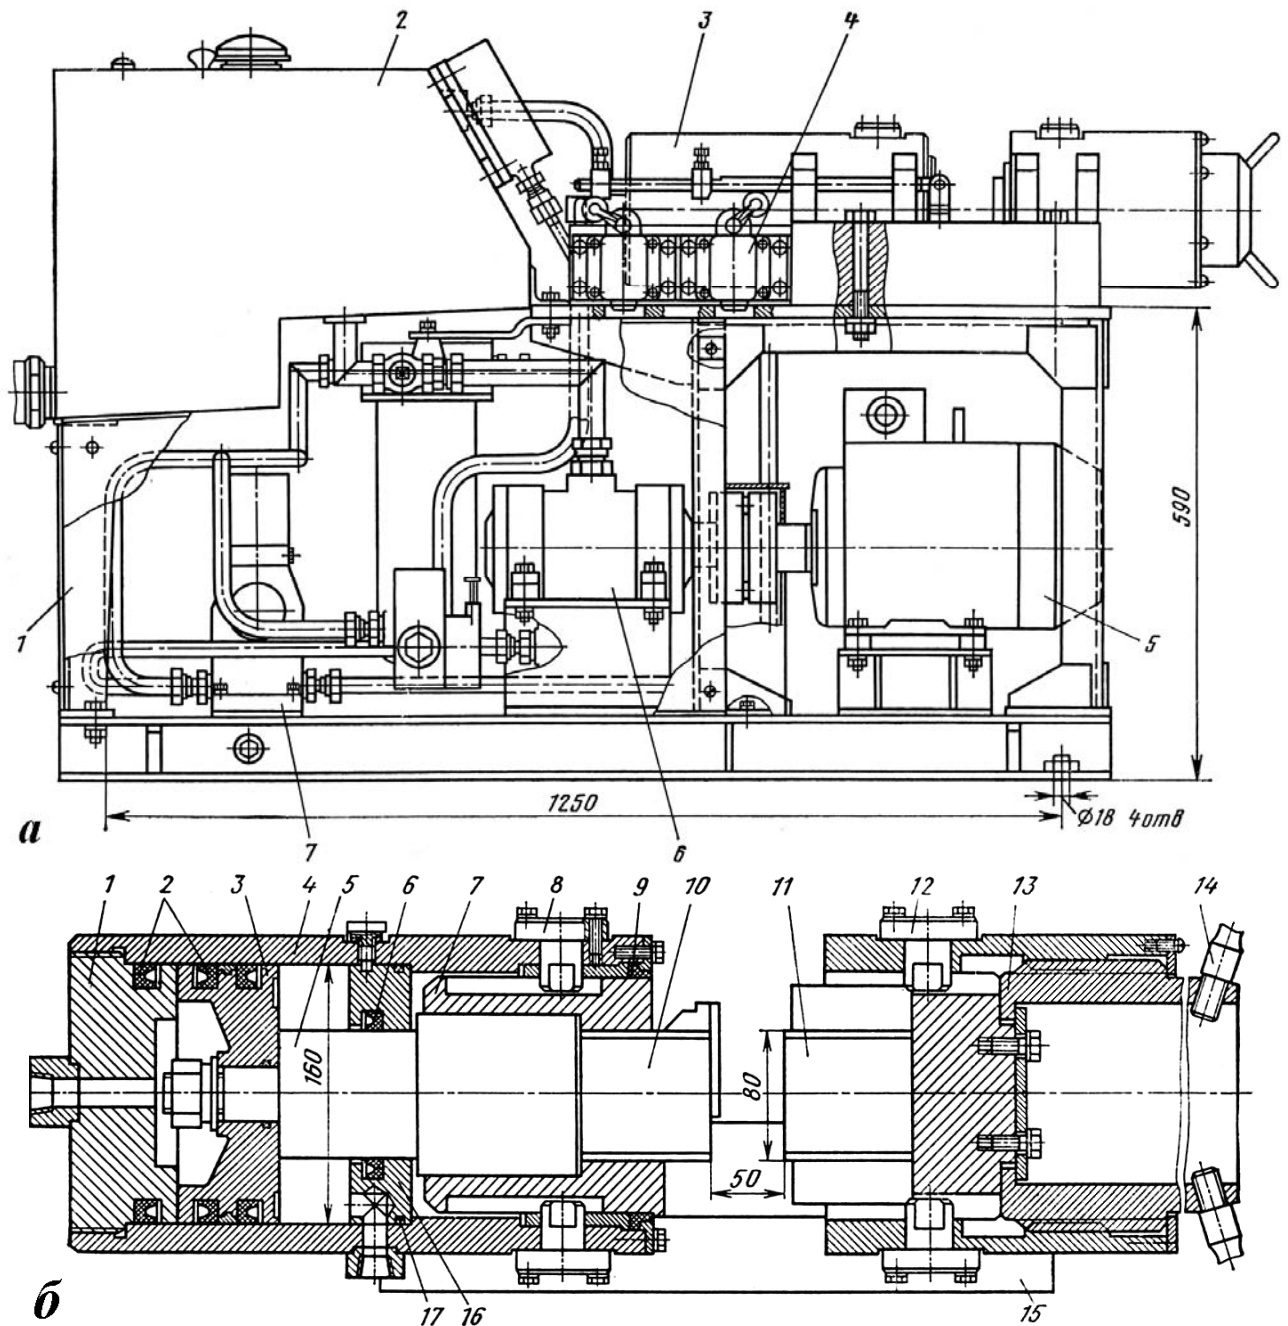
Станок СМЖ-133А для резки арматурных стержней:
